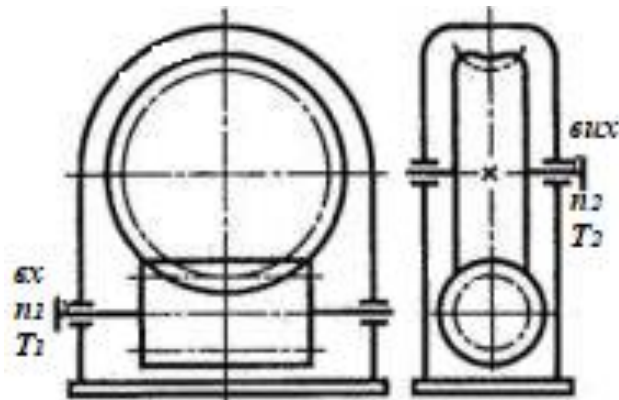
Кінематична схема черв'ячного редуктора
